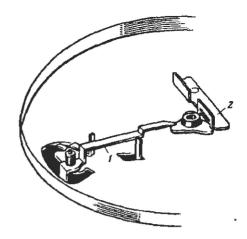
Рычаги автостопа и фиксации диска: 1 — рычаг сцепления; 2 — держатель диска
